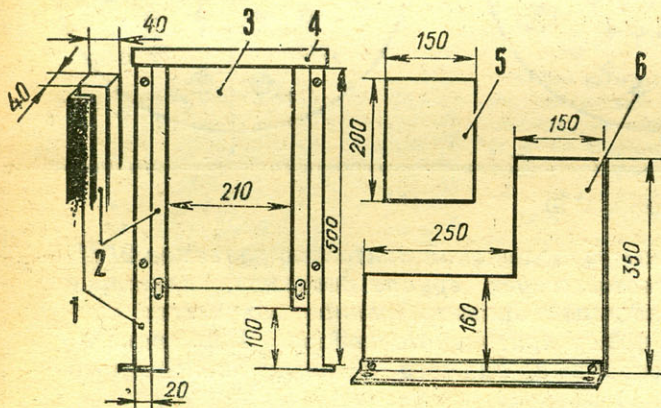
Прозрачная камера и панель корпуса прибора. 1 — металлический уголок, 2 — деревянный брусок, 3 — стеклянный лист, 4 — съемная крышка, 5 — подвижной пенопластовый поршень, 6 — декоративная панель из пластика.
